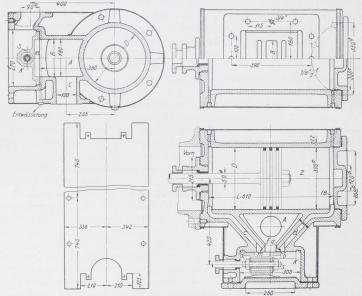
Zylinder mit Muschelschiebersteuerung. M. 1:15 und 1:25.
